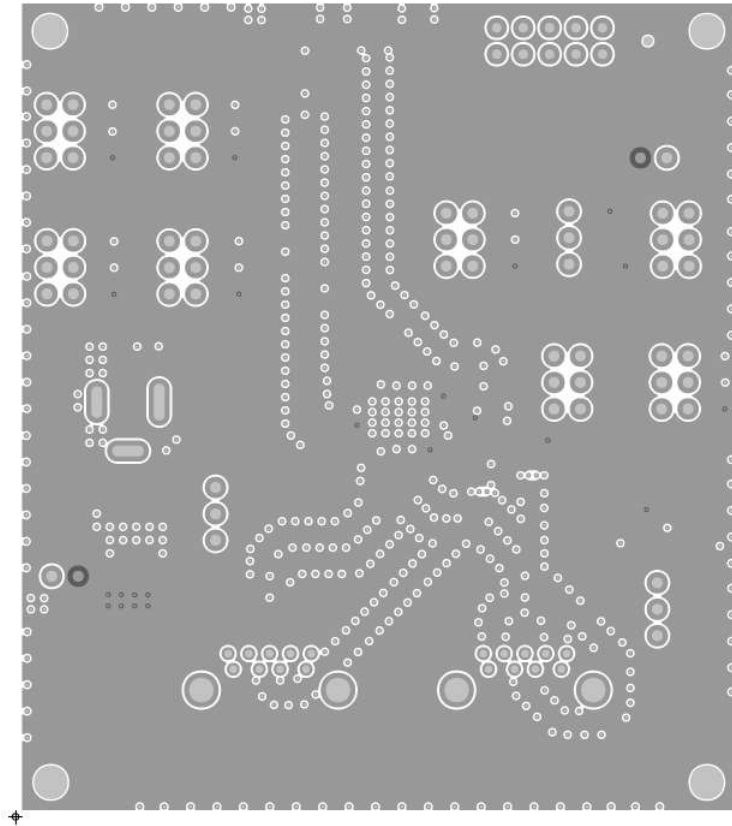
TUSB521Q1-EVM PCB 第 3 层 (电源)
